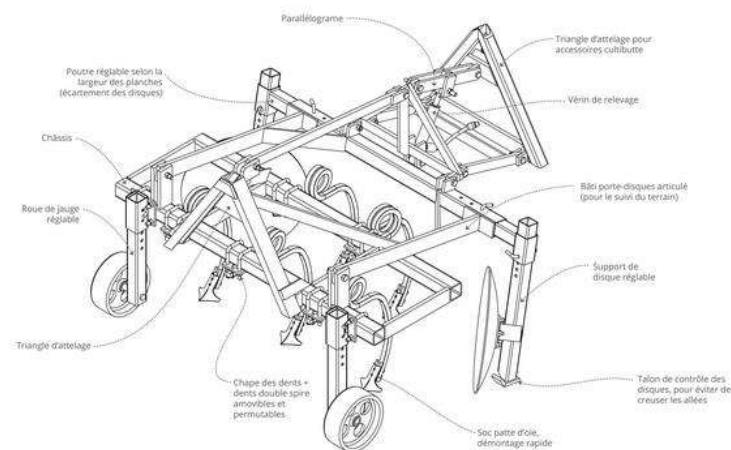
Le plan du cultibutte, accessible sur le site de l'Atelier paysan
